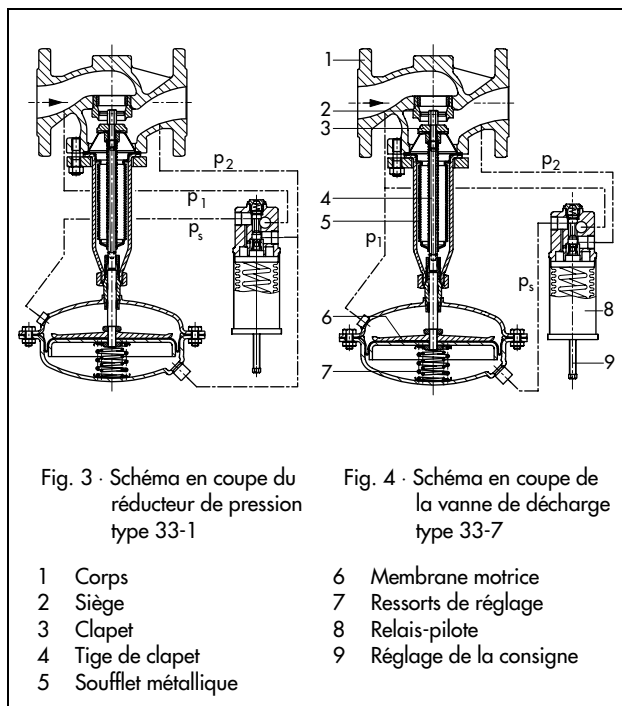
· Schéma en coupe du réducteur de pression type 33-1
